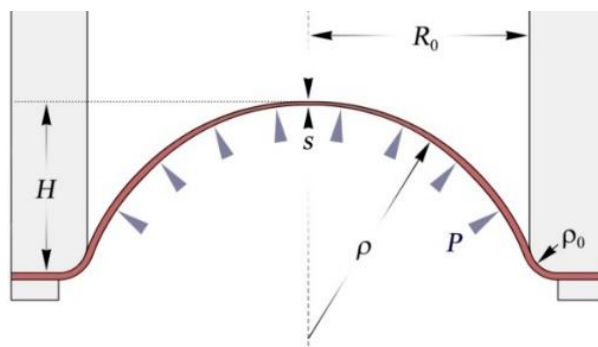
Схема процесса формовки в цилиндрическую матрицу
